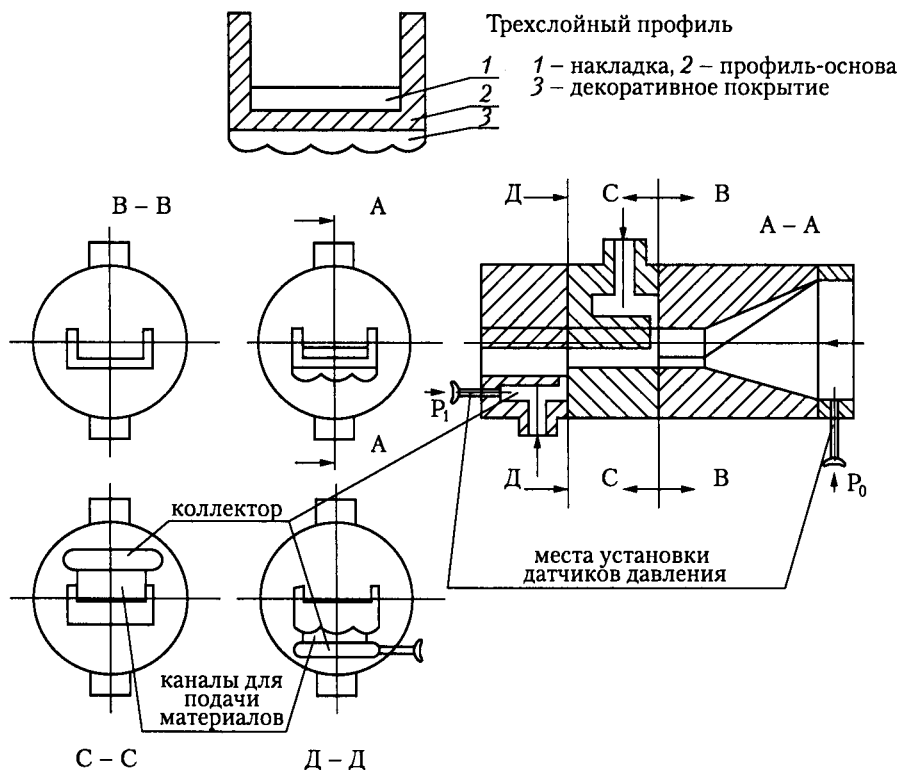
Схема экструзионной головки для изготовления трехслойного профиля [32]
